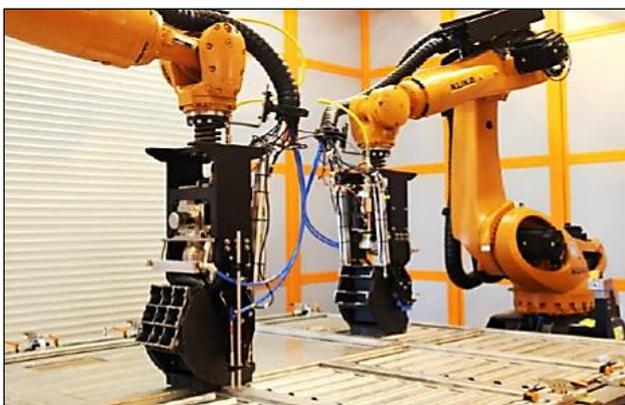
Оборудование для сварки боковых панелей вагонов метро.
